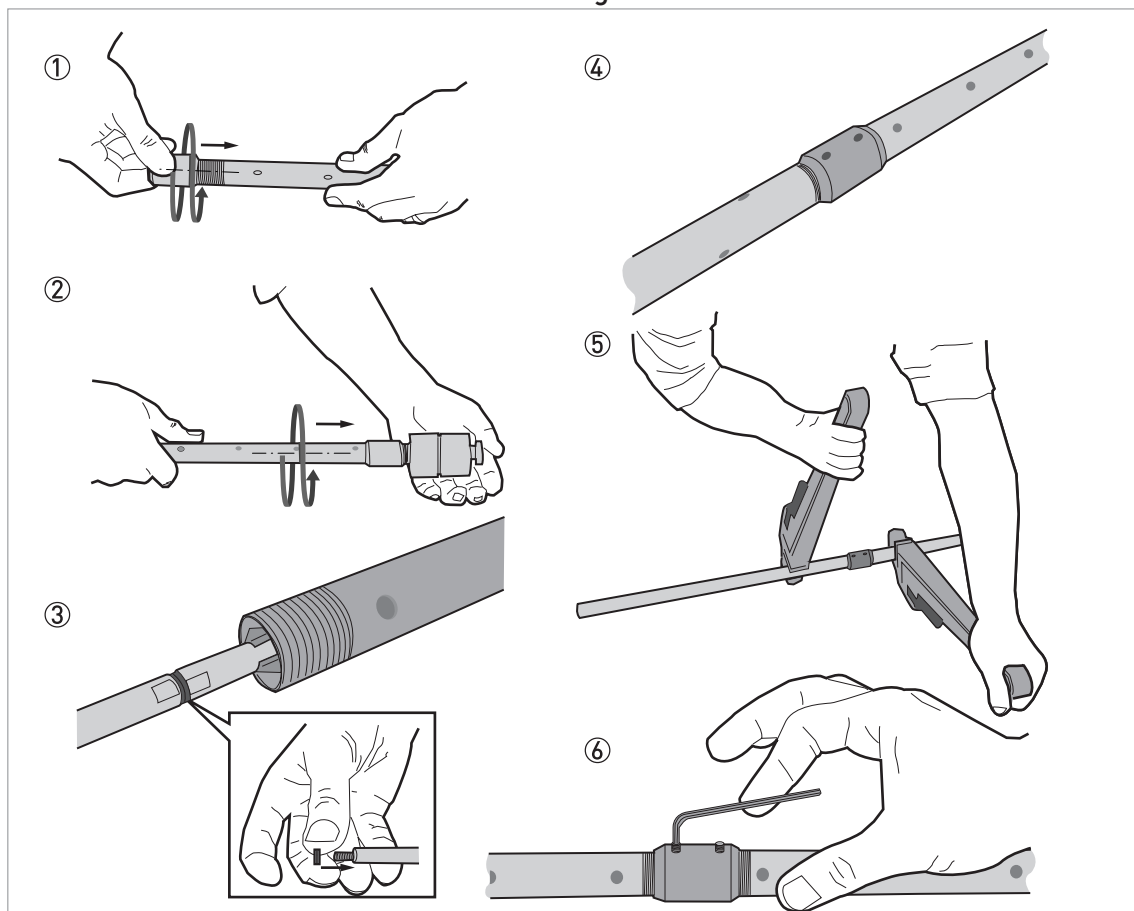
Cómo ensamblar la sonda coaxial segmentada: parte 2
